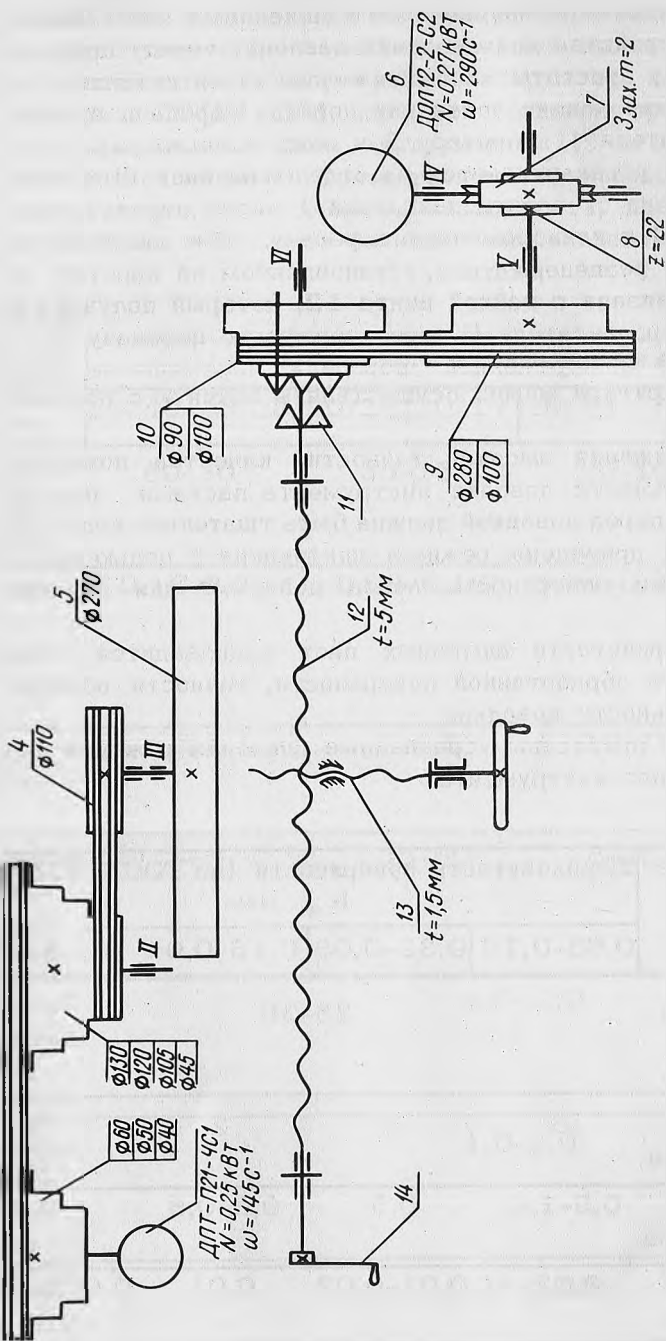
Кинематическая схема специальной установки для доводки инструмента: 1 — электродвигатель привода притира; 2, 3 — ступенчатые шкивы; 4 — шкив; 5 — притир; 6 — электродвигатель привода подачи ножа; 7, 8 — червячная передача; 9, 10 — ступенчатые шкивы клиноремной передачи; 11 — муфта; 12 — винт продольной подачи; 13 — винт поперечной подачи; 14 — маховичок.
